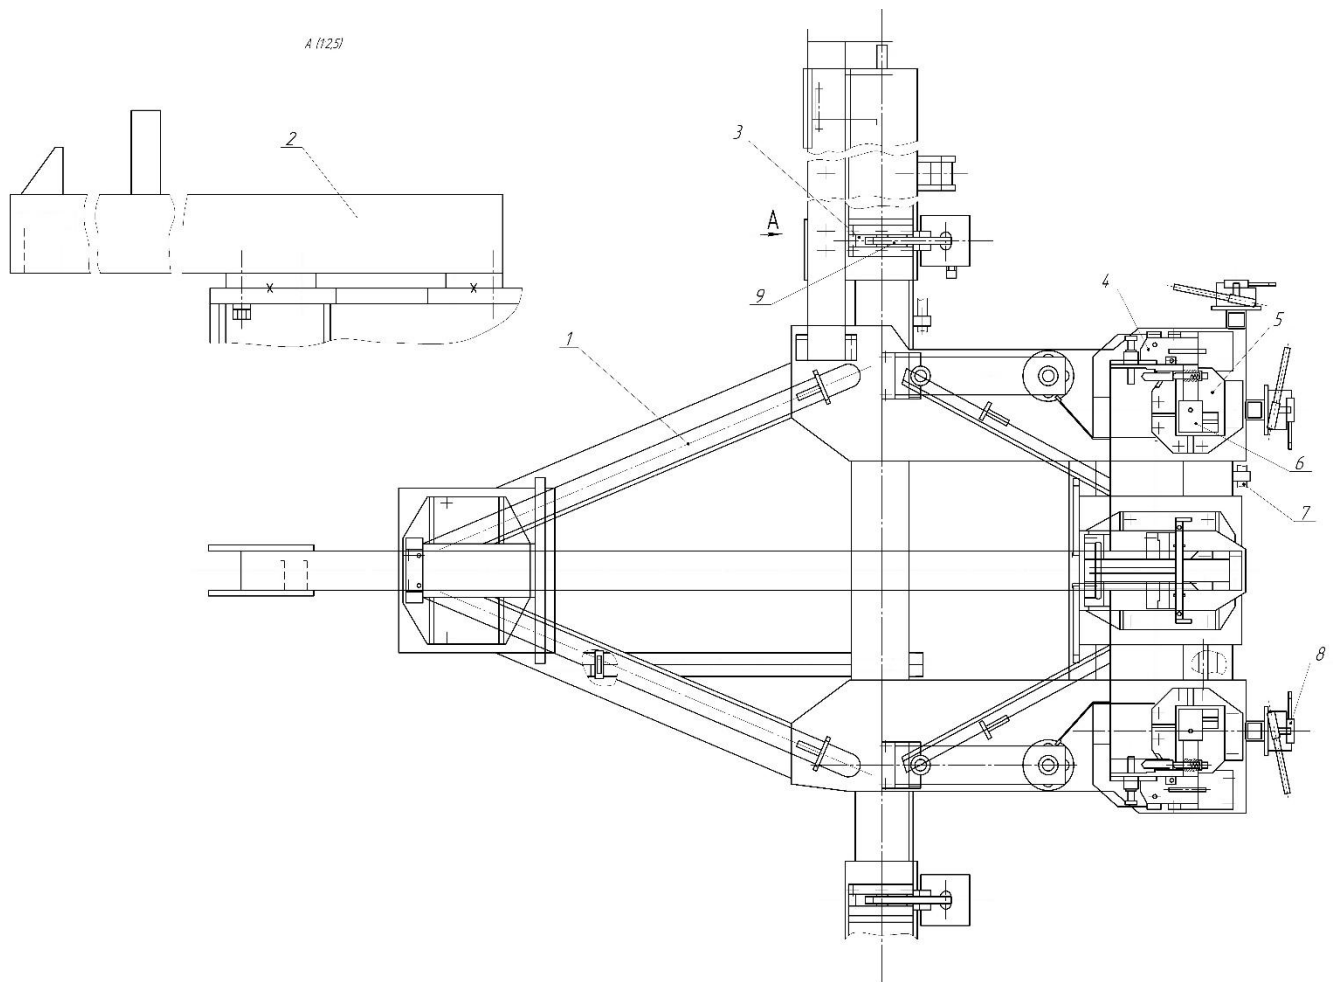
Складально-зварювальний кондуктор виготовлення відвалу
